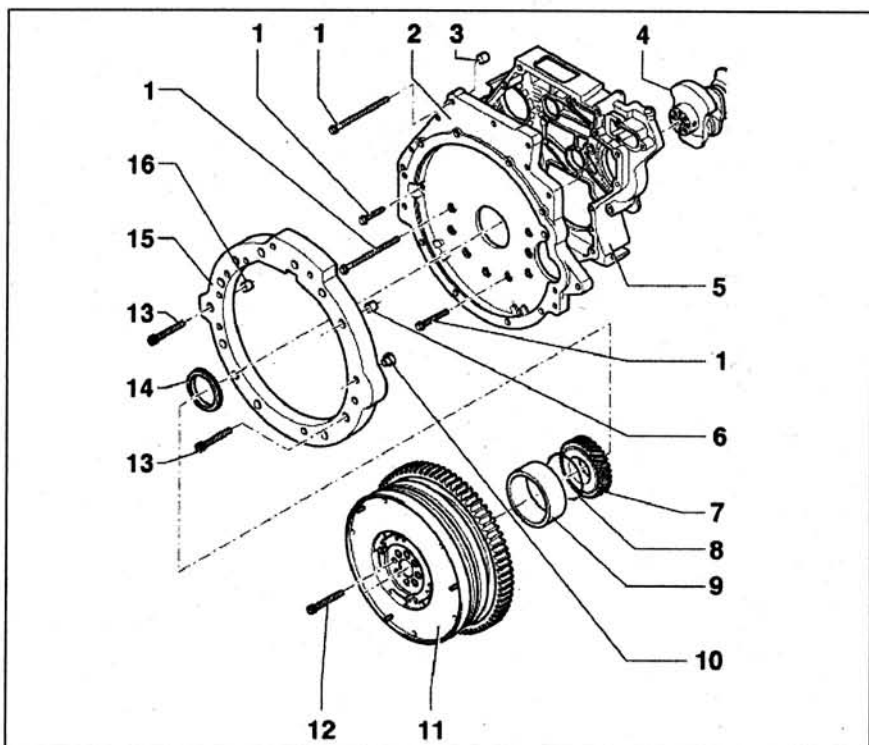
а. Шестерни привода и двухмассовый маховик:
